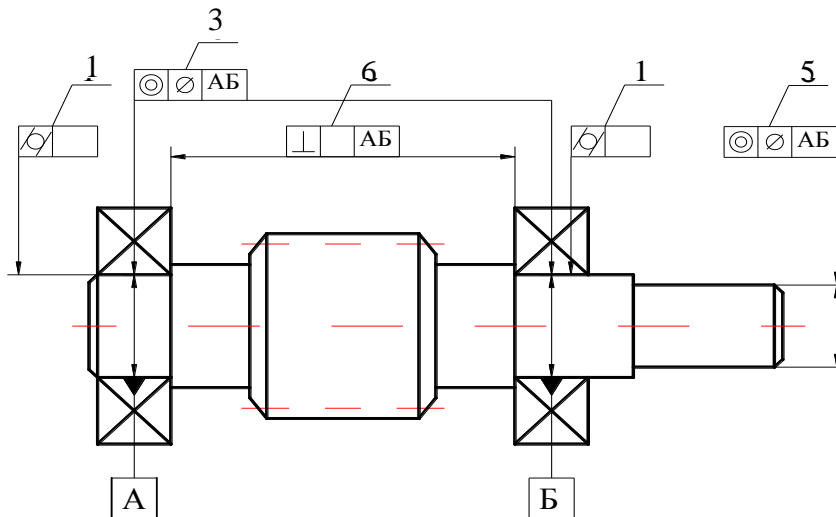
Условные обозначения баз, допусков формы и расположения червяка:
